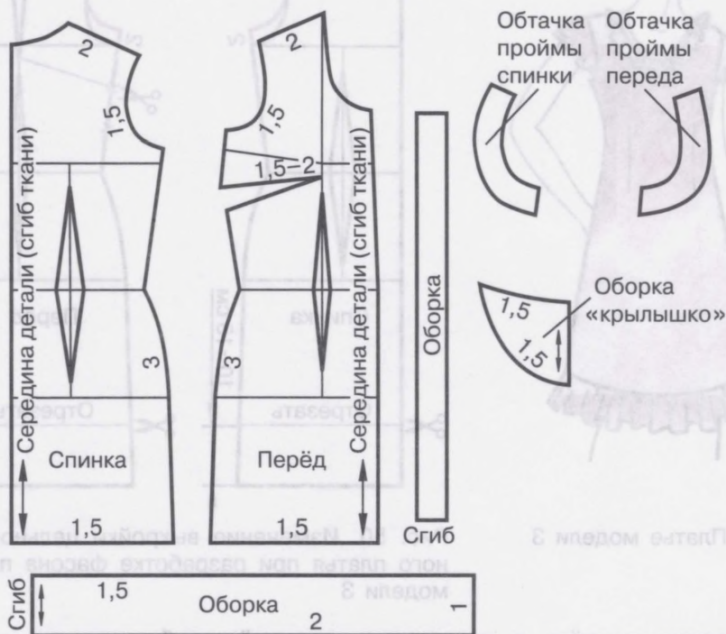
Подготовка деталей выкройки платья модели 3 к раскрою
